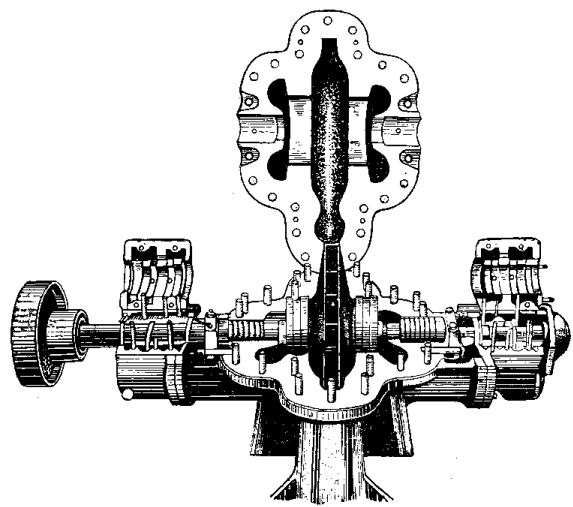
Одноколесный насос с двусторонним всасыванием и горизонтальным разъемом корпуса [5]
